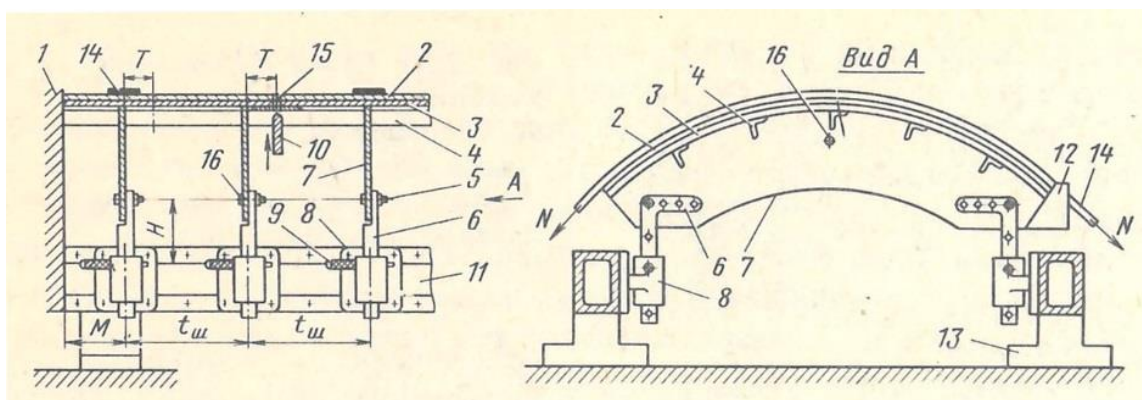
Универсальный стенд для сборки и сверления СО:
